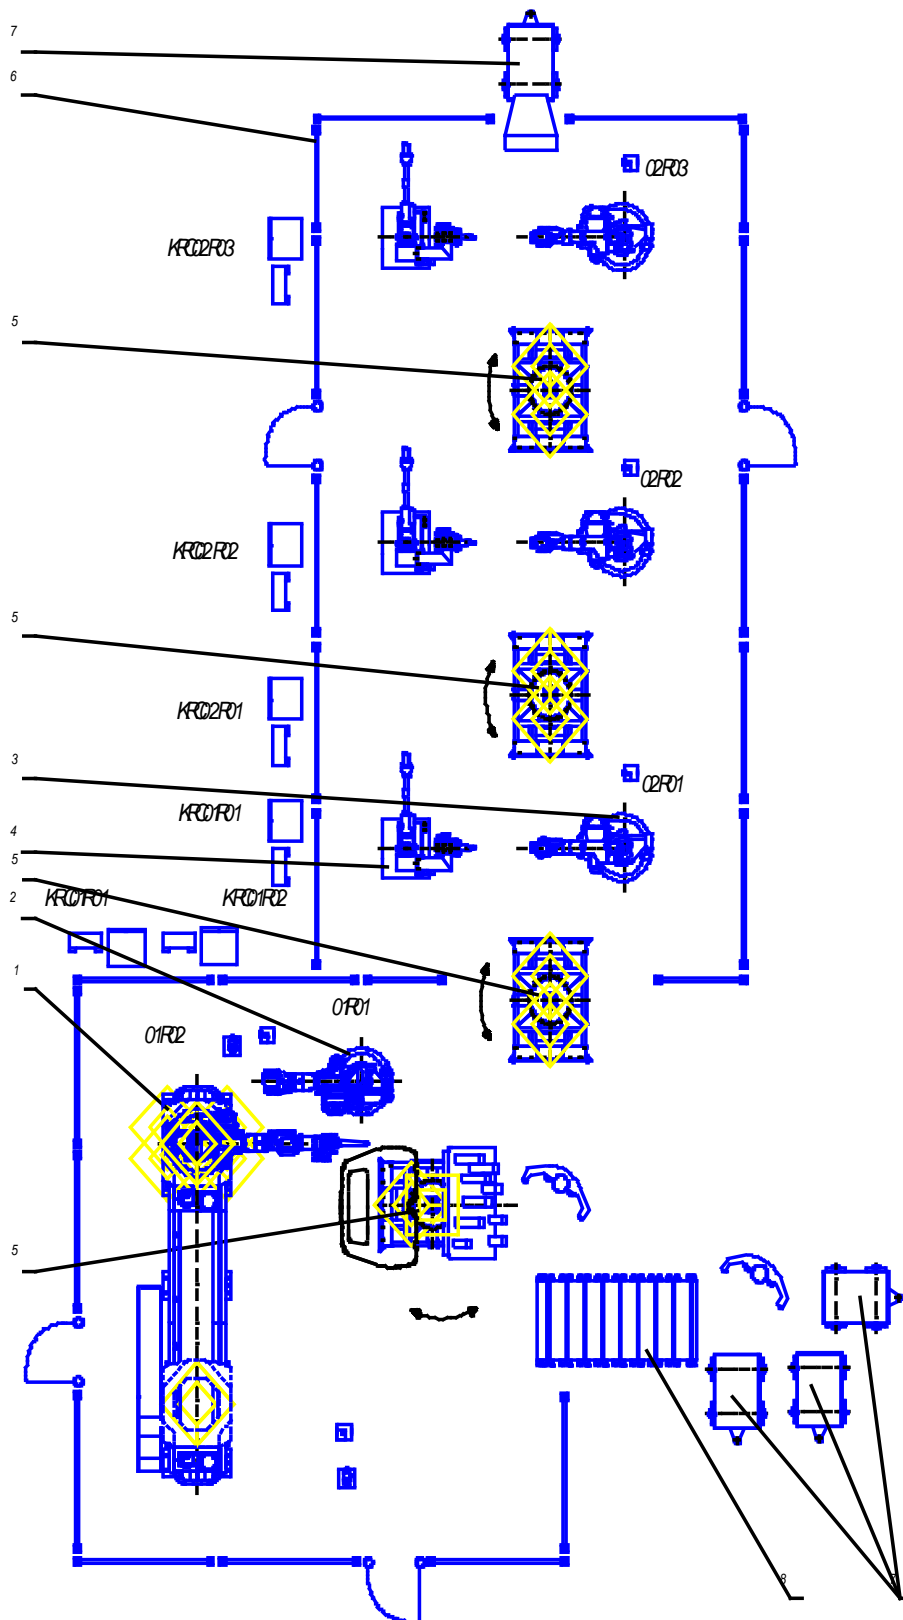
Участок сборки и сварки панели кабины задней ВАЗ 2345
